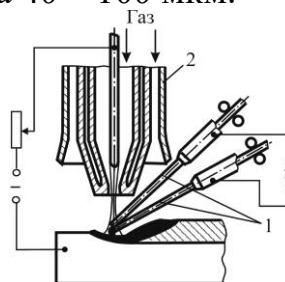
Схема плазменной наплавки с двумя присадочными проволоками
